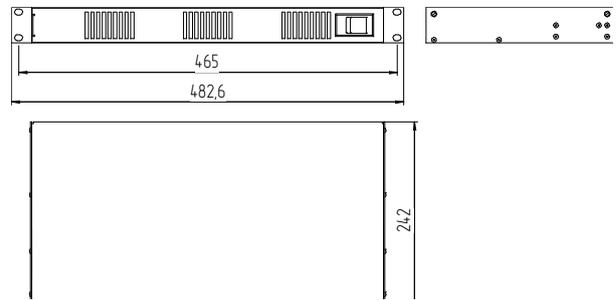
Габаритный чертеж ЩРЗ-7
